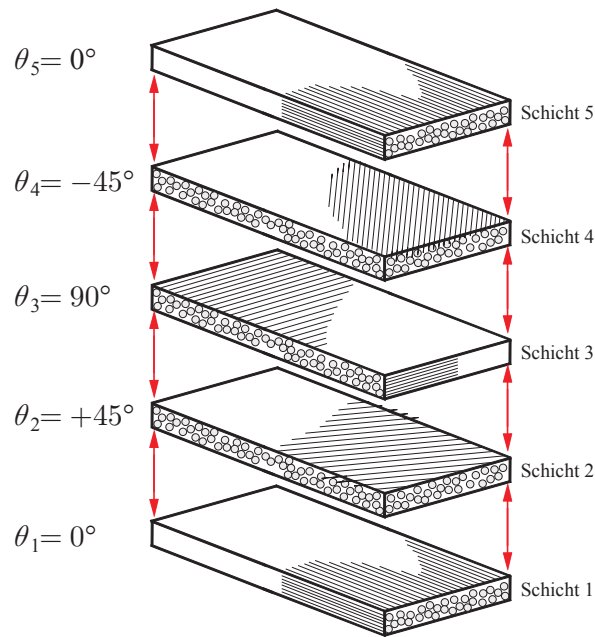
Explosionszeichnung eines Laminats [11]
